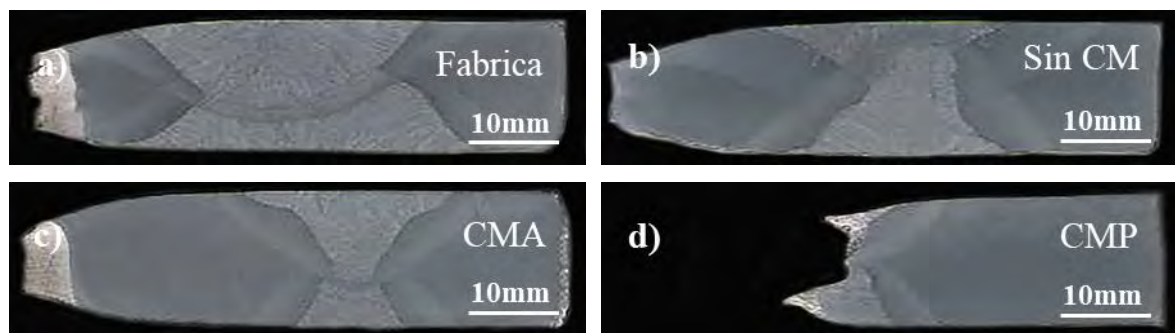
Macrografías de las fracturas de las pruebas de tensión en las soldaduras del acero API X-60; a) de fábrica por SAW, b) sin CM por GMAW, c) con CMA por GMAW y d) con CMP por GMAW.
